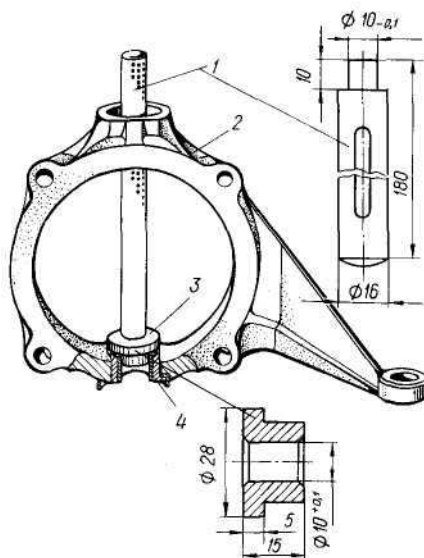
Выпрессовка корпусов втулок шкворней с втулками в сборе:
